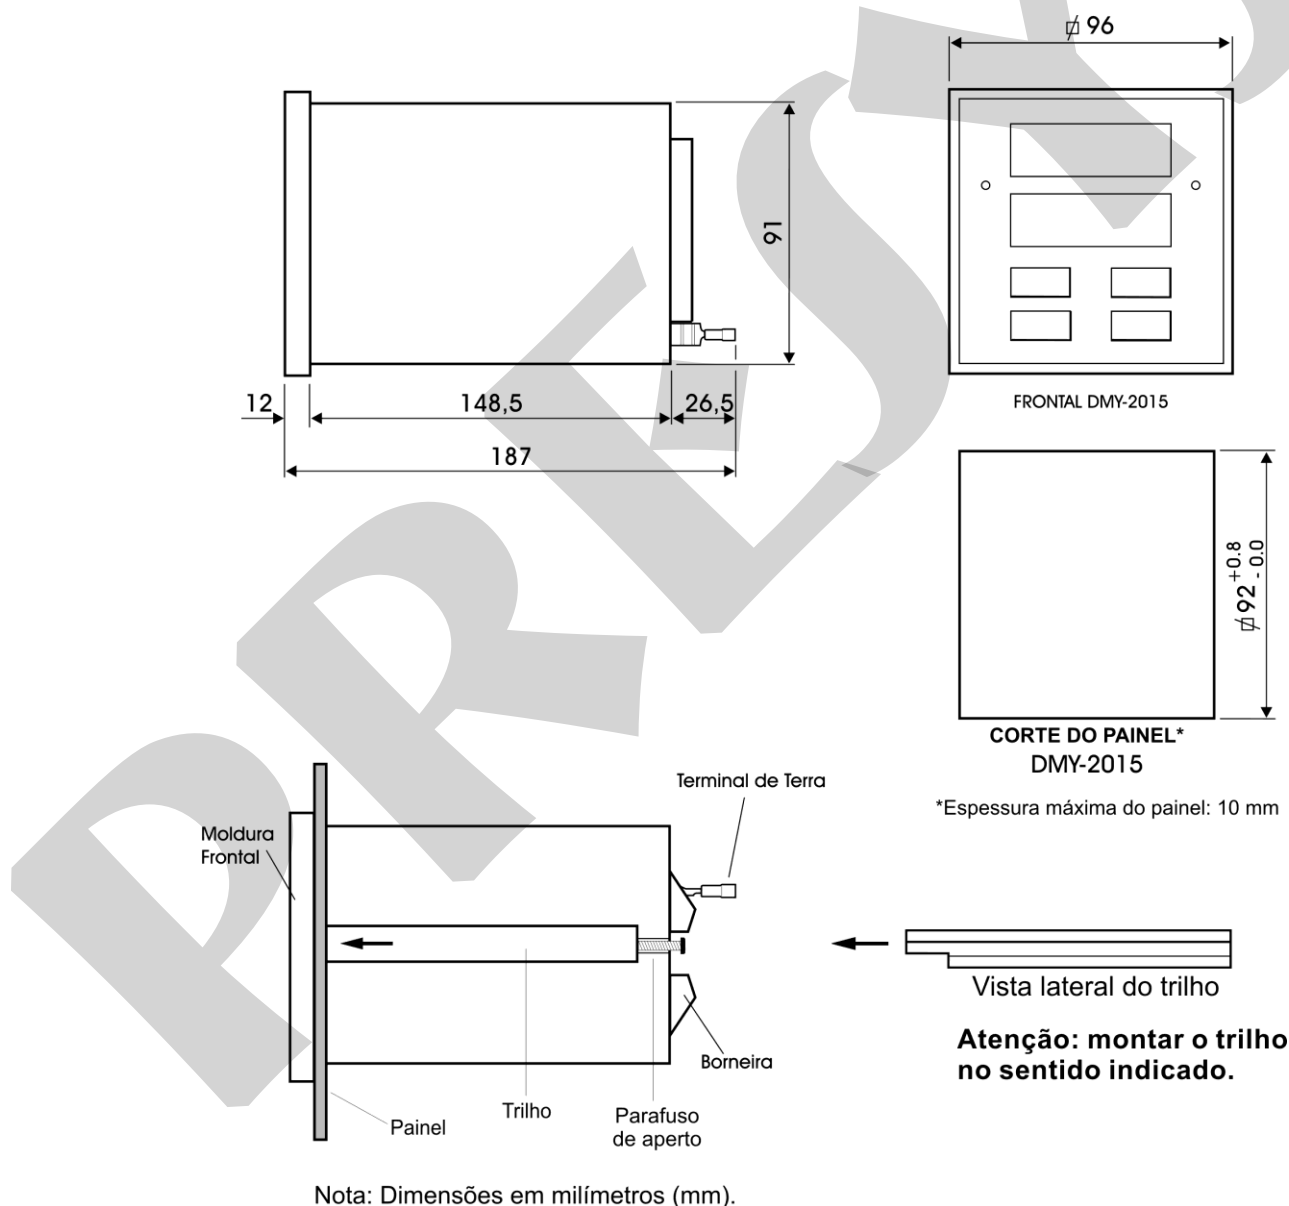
Desenho dimensional, corte e vista lateral da montagem no painel
